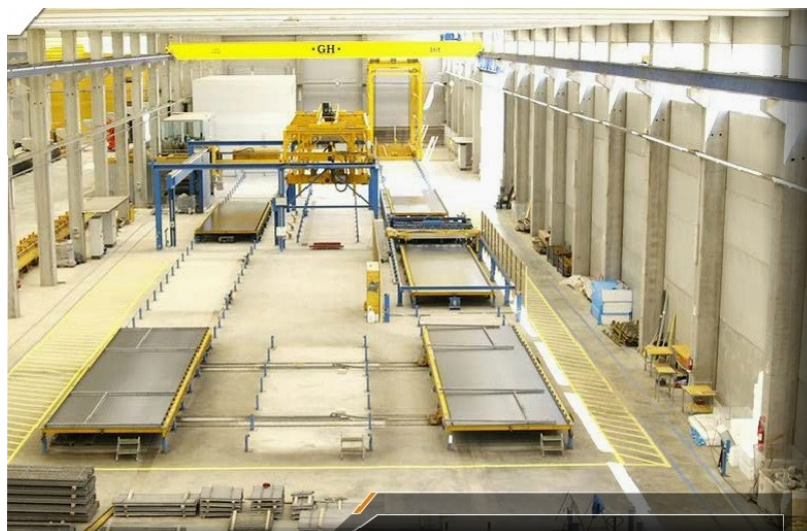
Nave 2, zona carrusel PAVI, Ref. PAVI
